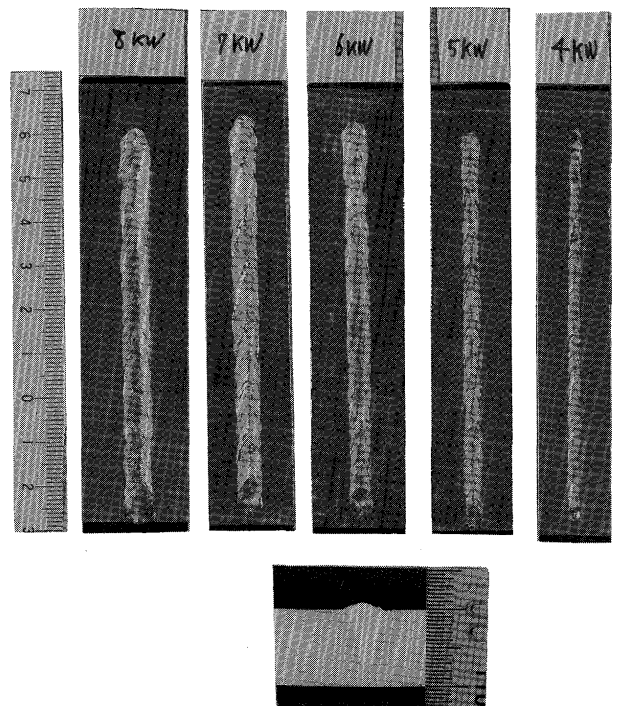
Schweißraupen-Erscheinung und ihr Querschnitt
